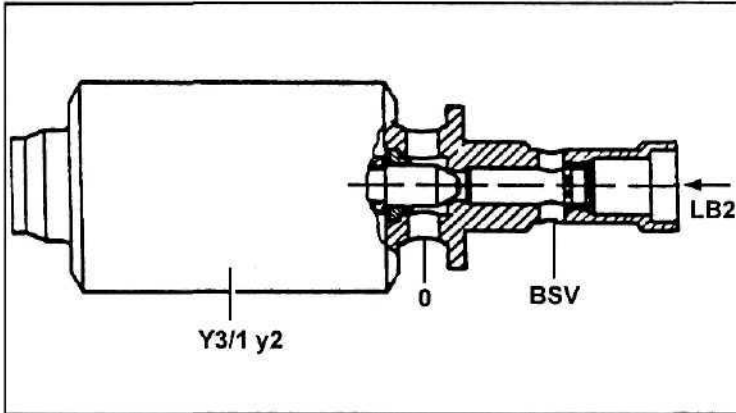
Регулировочный клапан (соленоид) Y3/1y2. 0 - слив; LB2 - из сервомотора ленточного тормоза B2; BSV - давление к клапану включения тормоза BS.
